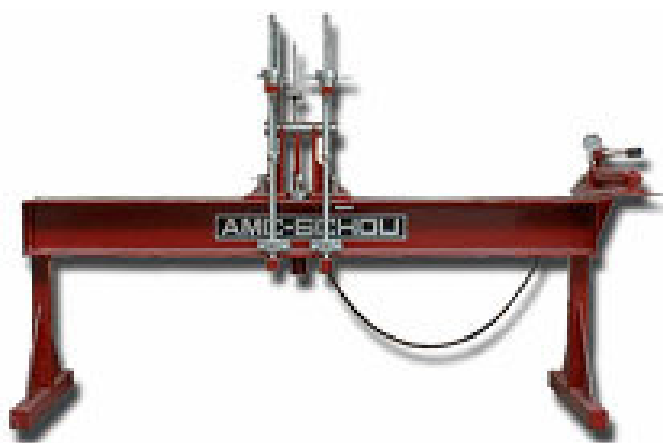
Гидравлический ручной пресс для правки валов СР 1800
